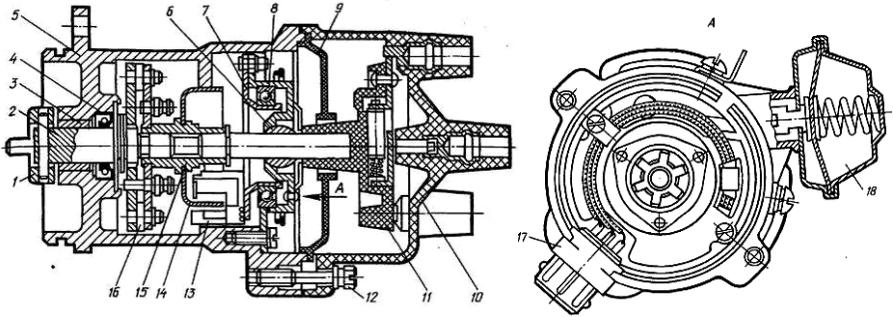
Датчик-розподільник: 1 – муфта; 2 – вал; 3, 6 – втулки; 4 – сальник; 5 – корпус; 7 – рухома пластина; 8 – підшипник; 9 – перегородка; 10 – кришка; 11 – бігунець; 12 – гвинт; 13 – датчик Холла; 14 – ротор-шторка; 15 – втулка; 16 – відцентровий регулятор; 17 – штекер; 18 – вакуумний регулятор
